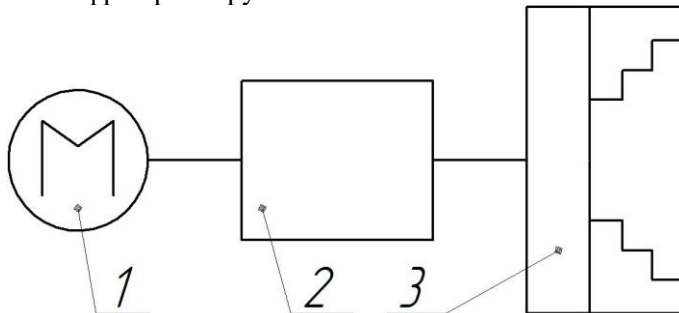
Принципова схема автоматизованого поворотного пристосування
